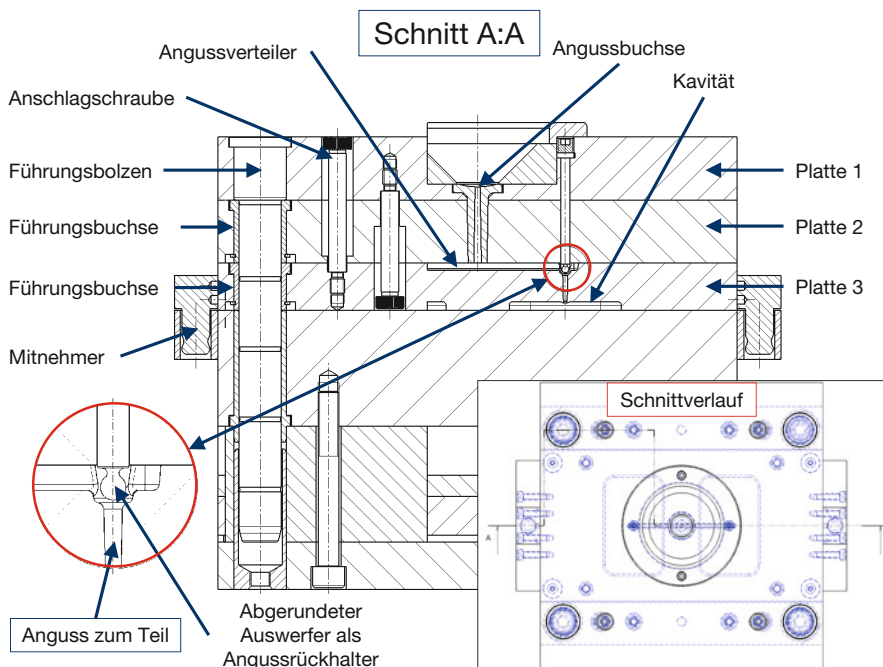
Schnitt durch ein Drei-Platten-Werkzeug
